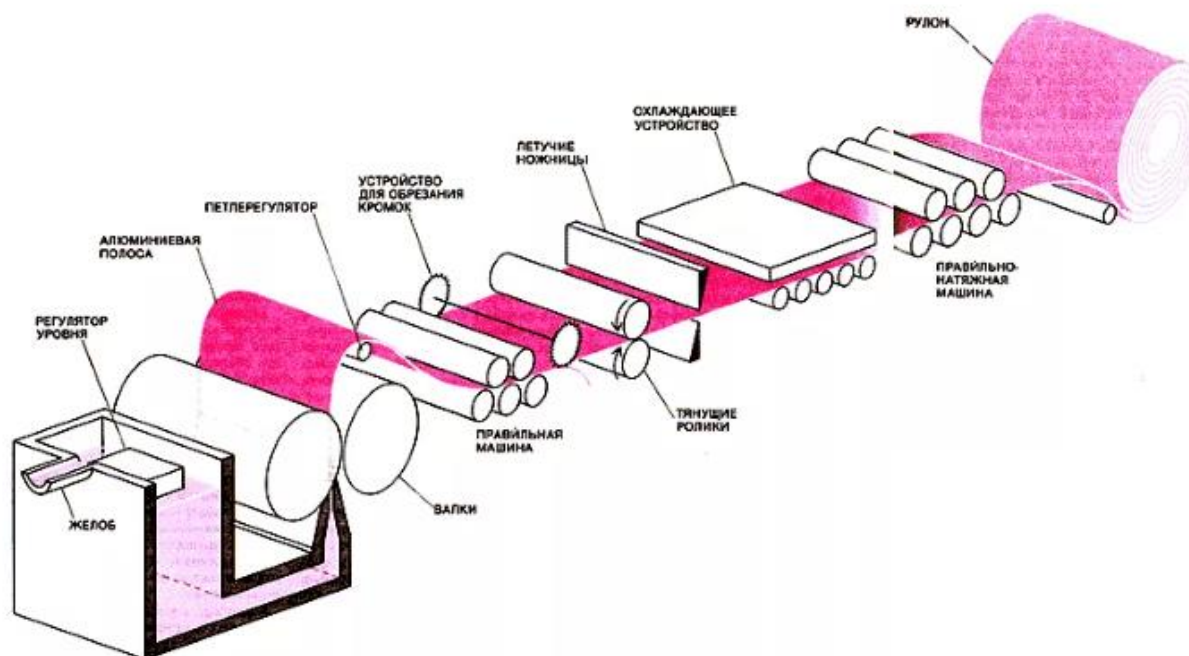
Схема агрегата валковой-разливки-прокатки
